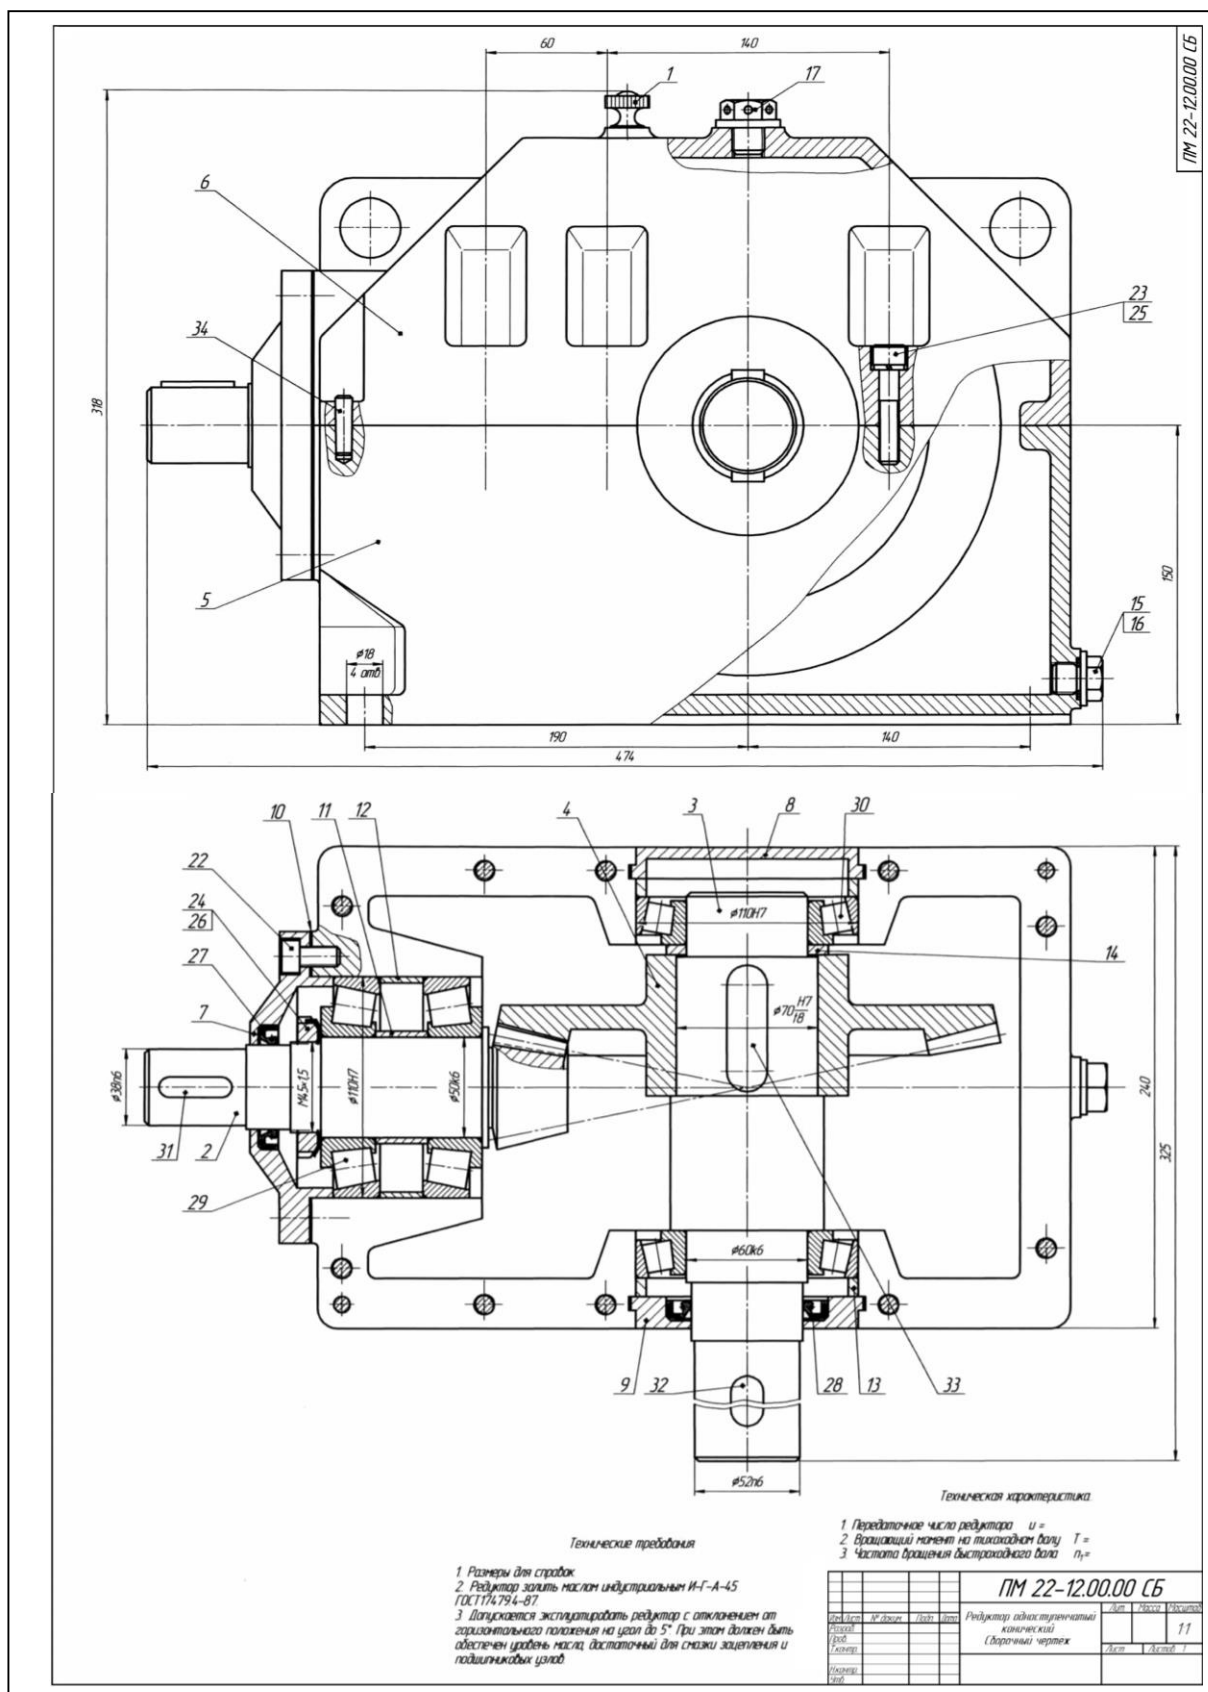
Пример сборочного чертежа одноступенчатого конического редуктора
